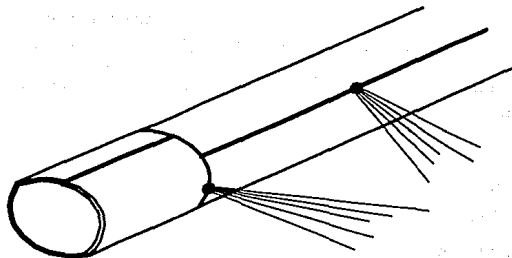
Poro en soldadura transversal y/o longitudinal.
